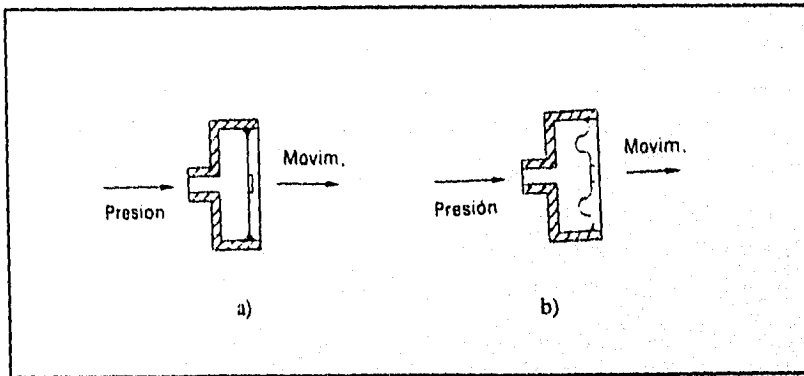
Diafragmas; a) Tipo plano, b) Tipo ondulado.
